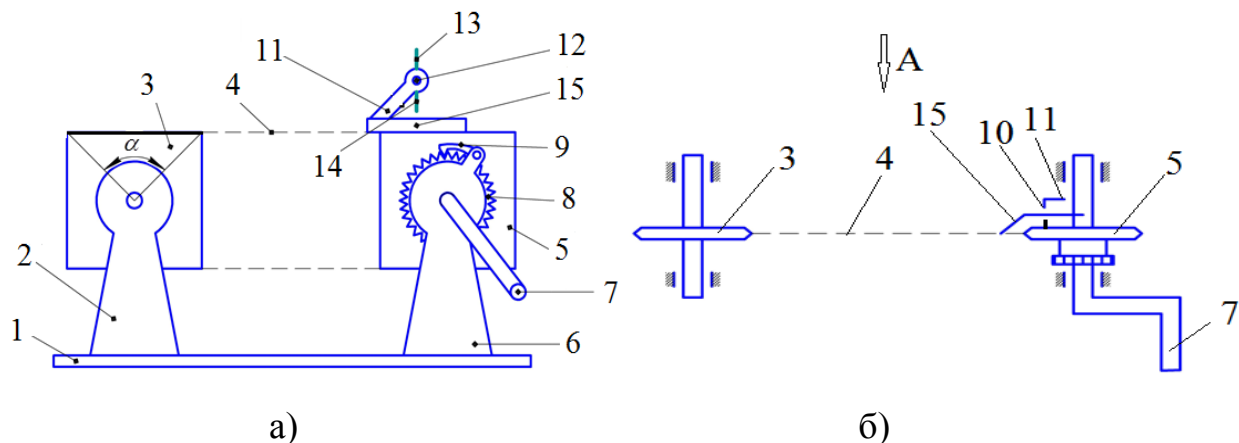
а, б – Учебный прибор для демонстрации изменения поступательной скорости движения цепи в цепной передаче 1 – рама; 2 – опора; 3 – ведомая звездочка; 4 – цепь; 5 – ведущая звездочка; 6 – опора; 7 – рукоятка; 8 – звездочка храпового останова; 9 – собачка; 10 – кронштейн; 11 – стрелка; 12 – ось; 13 – верхний участок отвеса; 14 – нижний участок отвеса; 15 – линейка
